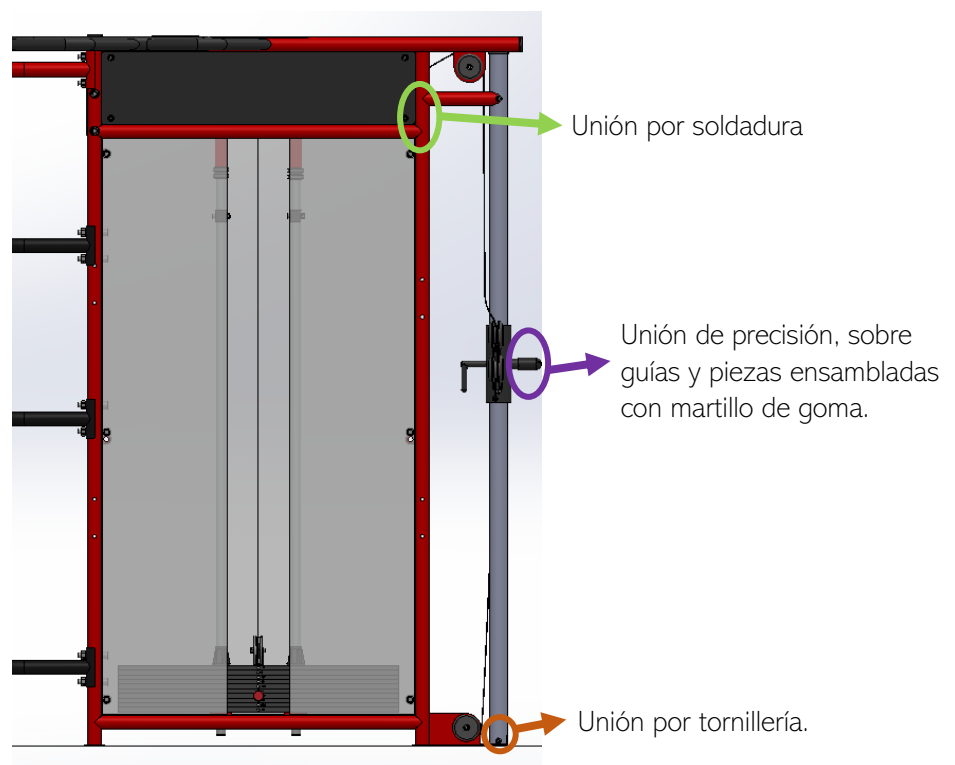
Soldadura y uniones de ensamblaje del subconjunto 1. Fuente: Elaboración propia
